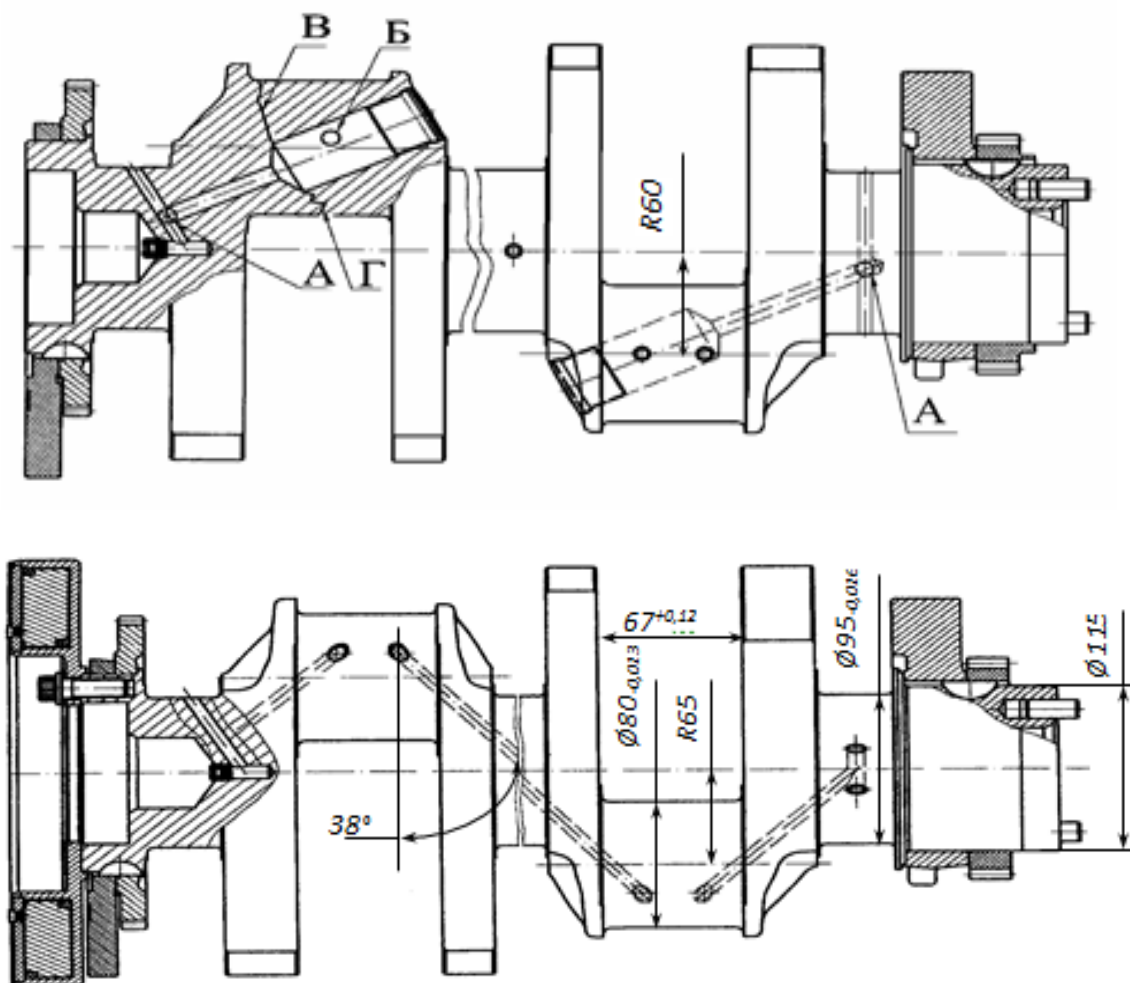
Коленчатые валы двигателей КАМАЗ
